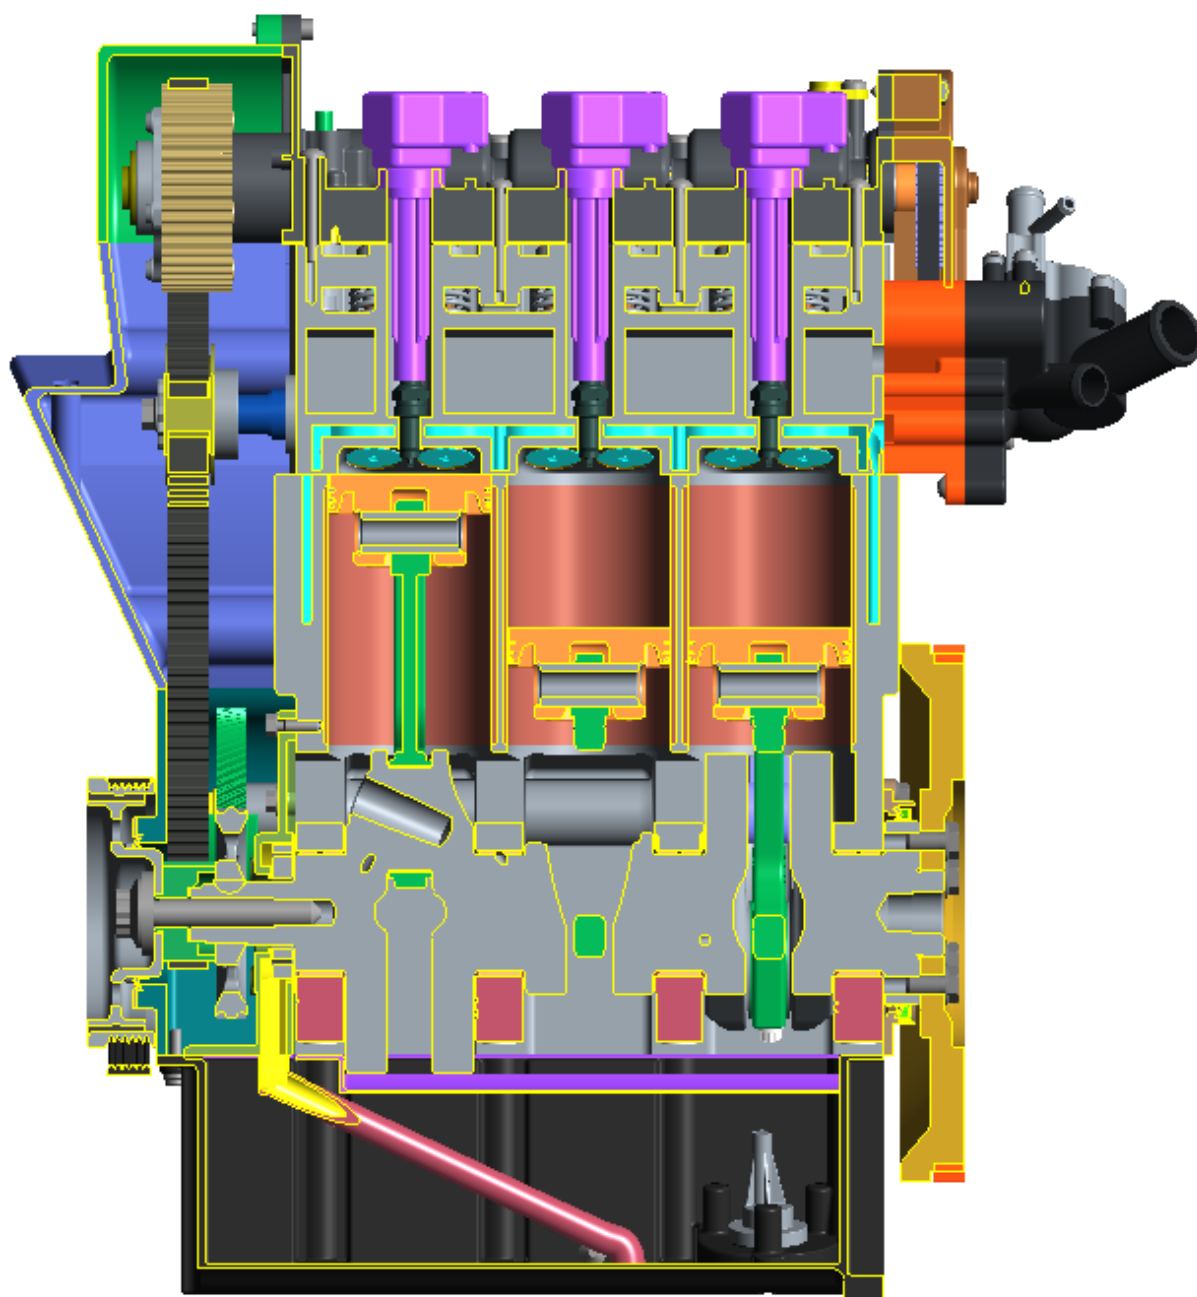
Mazání hlavních a ojnicích ložisek čtyřválcového motoru
